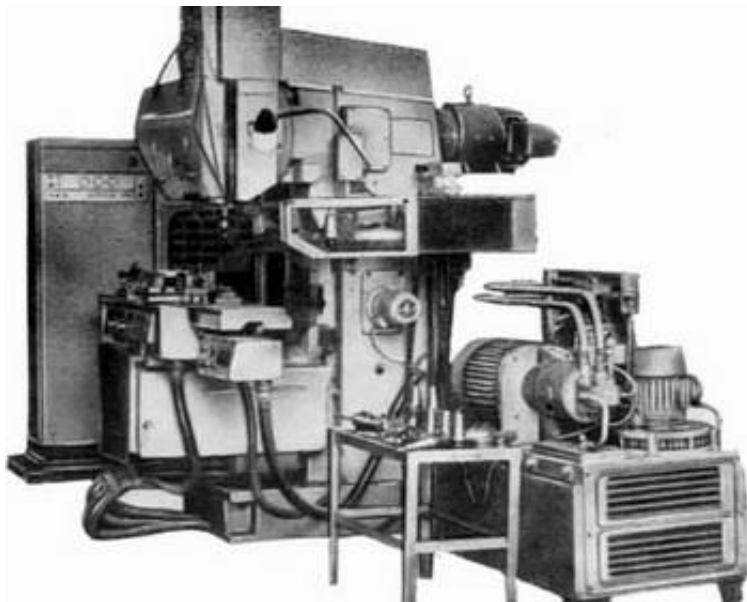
Общий вид вертикально-фрезерного станка 6P11MФ3
